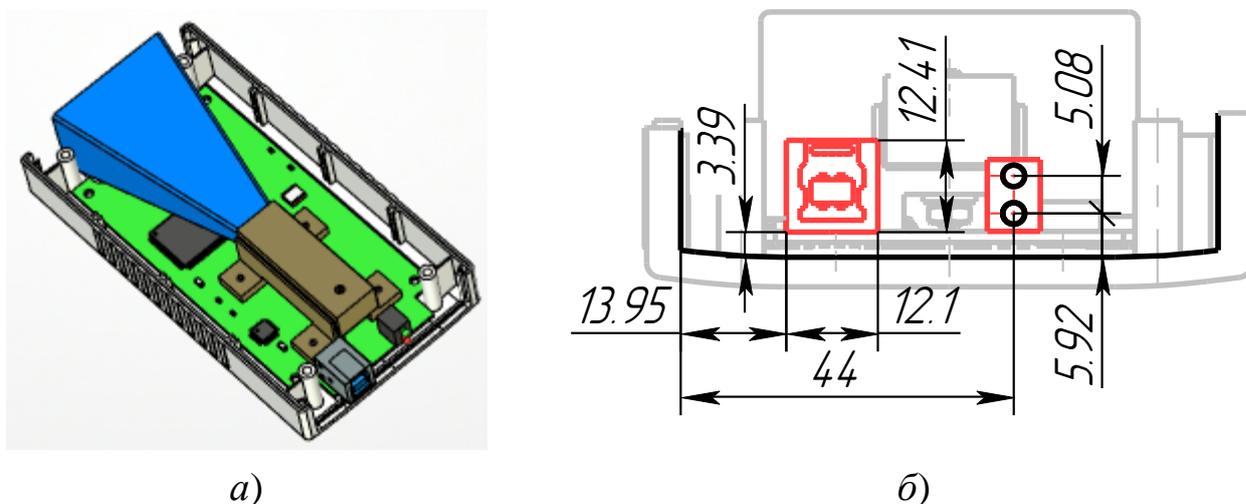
Печатный узел в корпусе (а) и размеры для выполнения отверстий (б)
